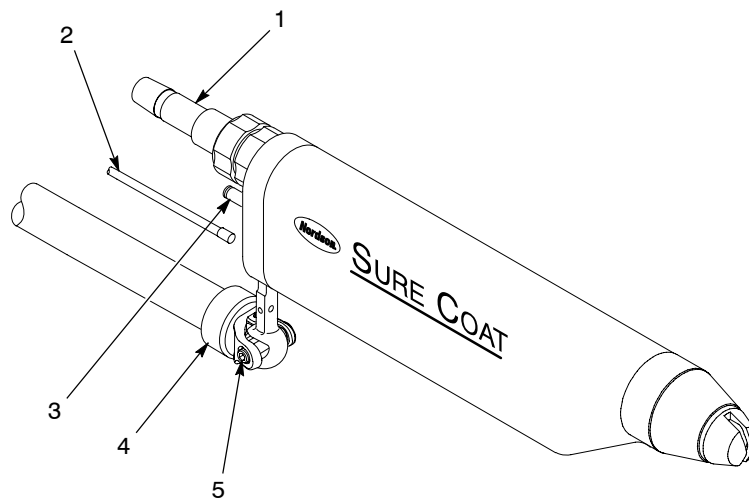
Rimozione della pistola con montaggio su tubo
